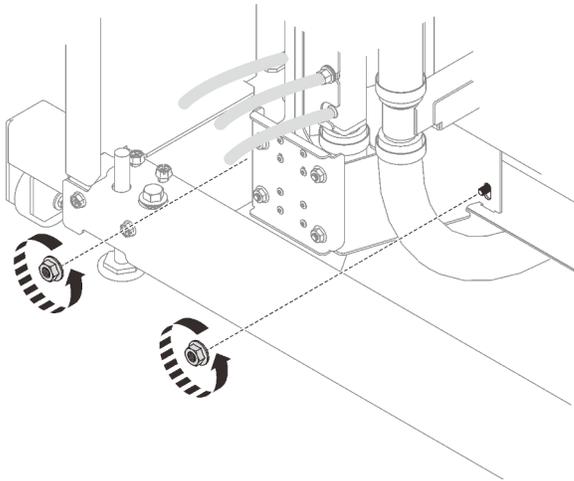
Entfernen der Muttern an der unteren Montagehalterung für die Rackleitung
